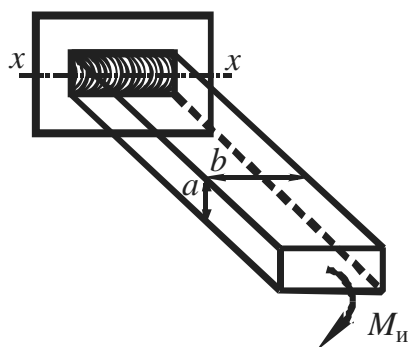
Схема стыкового сварного шва, нагруженного изгибающим моментом
